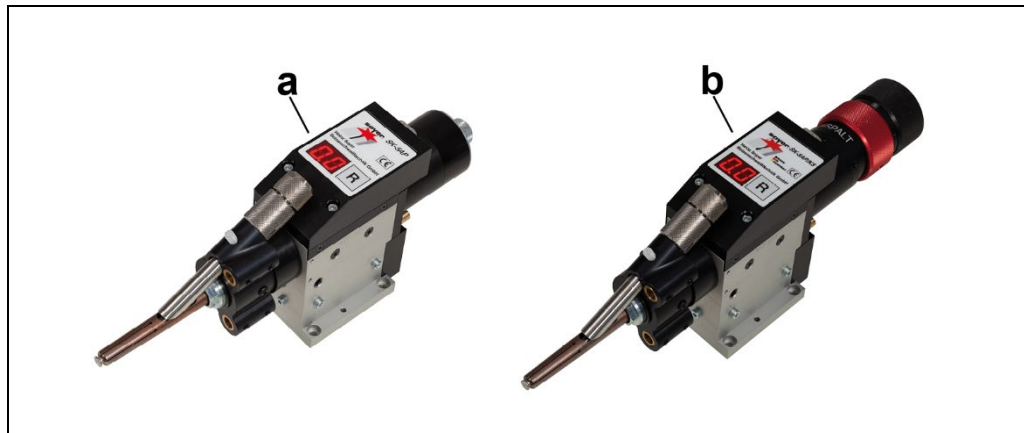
Bolzenschweißkopf SK-5AP/KS
